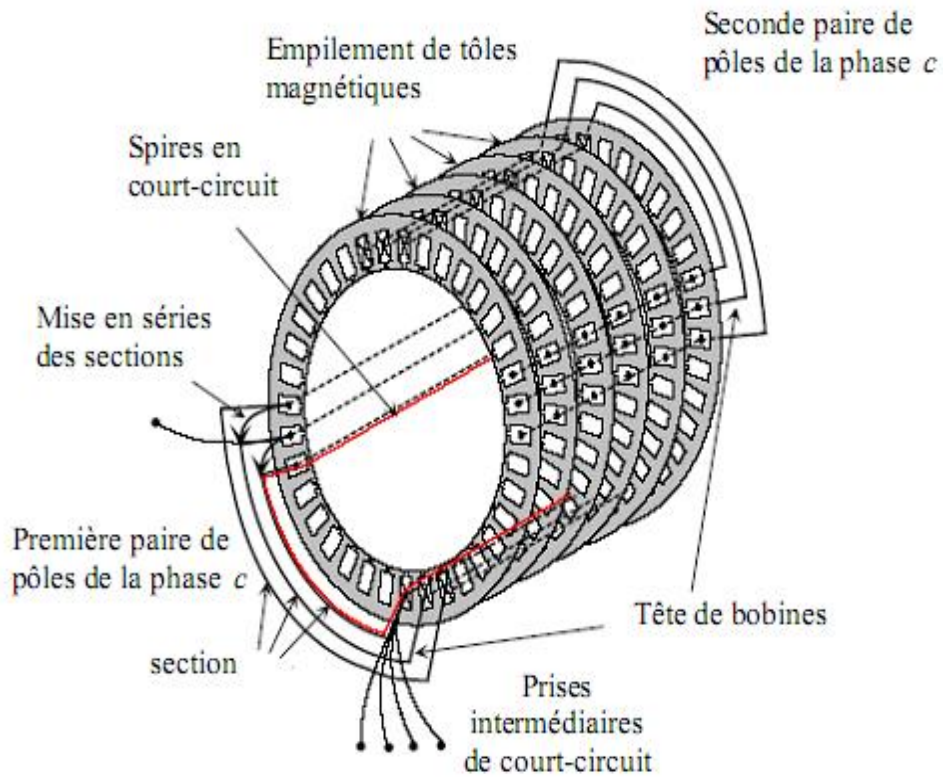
Vue schématique en perspective du stator (circuit magnétique, conducteurs d'encoches, tête de bobines). (Enroulement statorique d'une machine a 4 pôles) [11].
